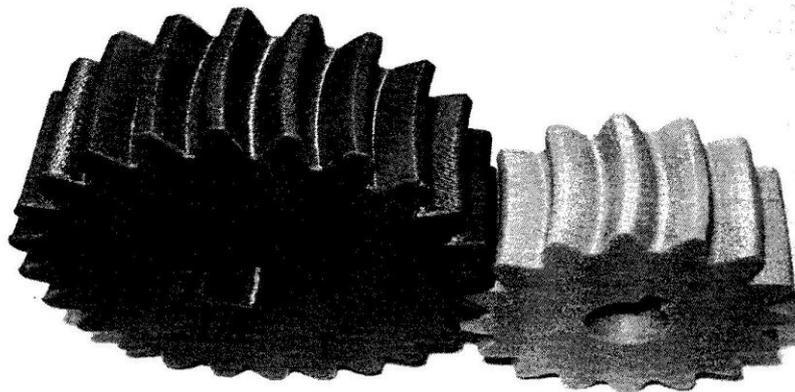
Образцы цилиндрических зубчатых колес с круговым зубом, изготовленные по FDM технологии
